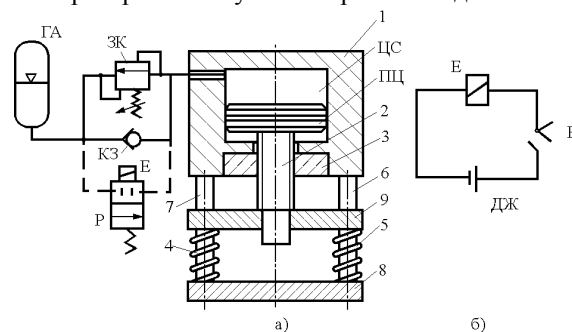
Принципова конструкція одноциліндрового пристрою –а; можлива електрична схема – б
